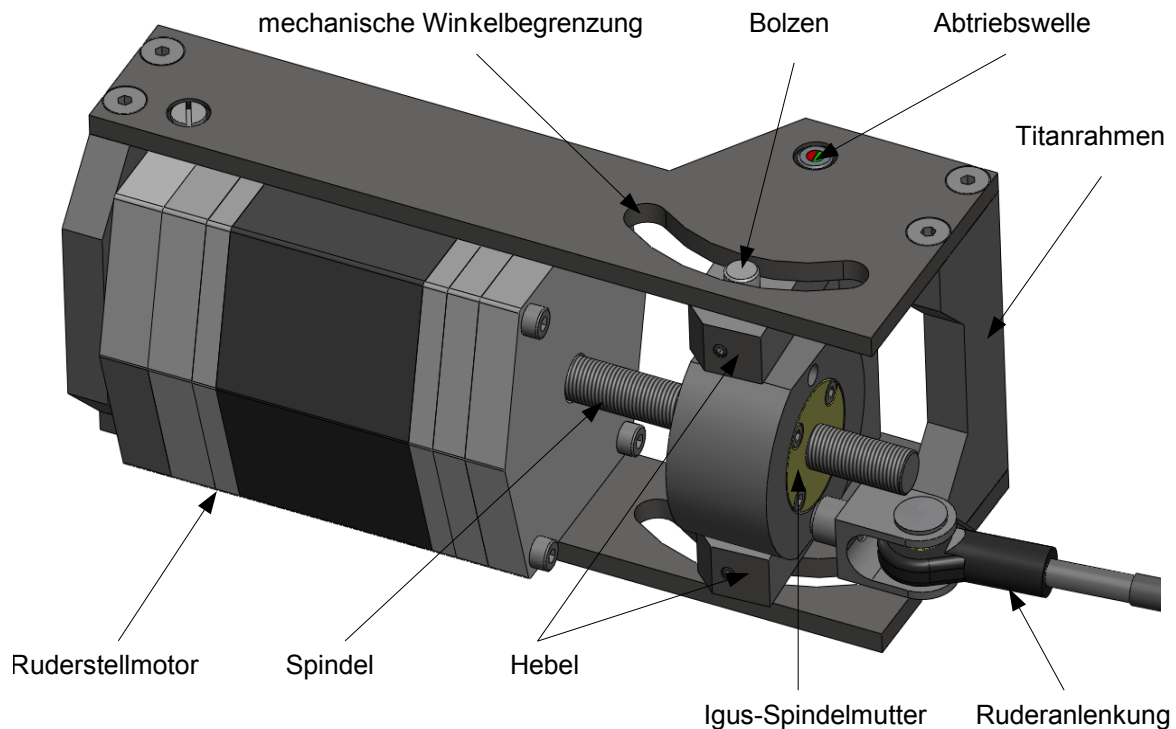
CAD-Ansicht des Ruderstellmoduls
